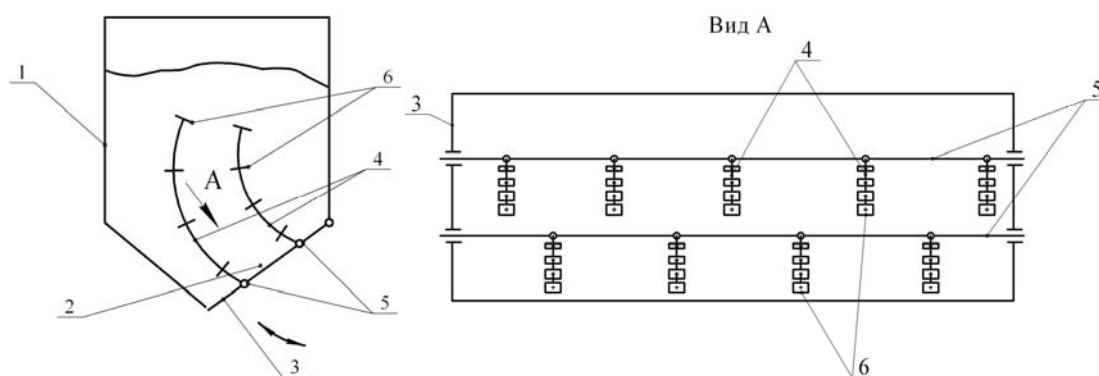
Схема выгрузного устройства с рыхлящим затвором: 1 – корпус бункера; 2 – выпускного отверстия; 3 – крышка; 4 – стержни; 5 – оси; 6 – дискообразные элементы (пластины)
